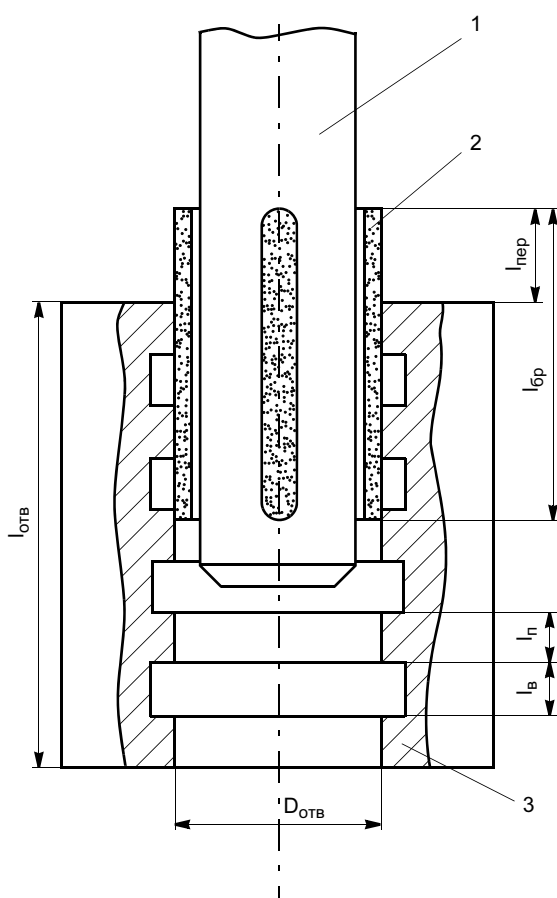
Схема хонингования прерывистых отверстий: 1 — хонголовка; 2 — абразивный брусок; 3 — обрабатываемая заготовка
